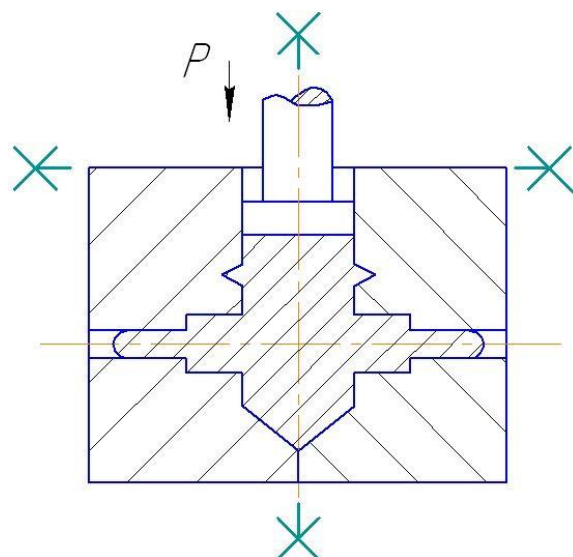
Штамповка поковок прошивкой в разъемной матрице
